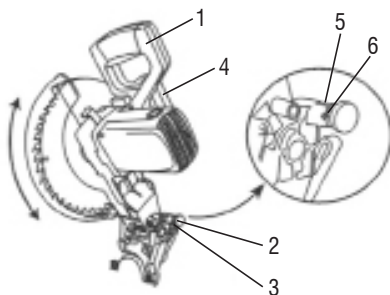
Transporte e armazenagem do cabeçote da máquina
